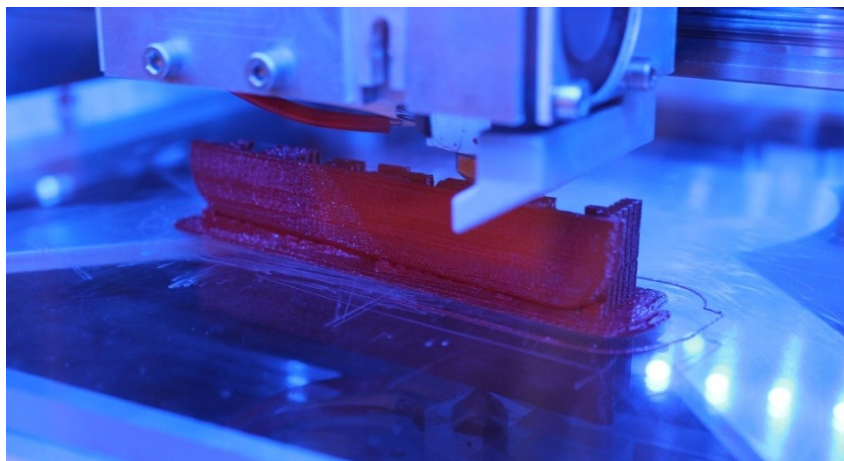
Zobrazený Raft - 2 a Skirt - 1
